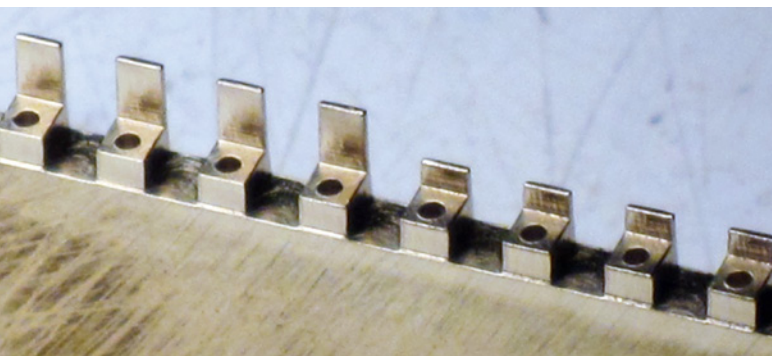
Fräsgrat mit rotierender Drahtbürste entfernt; 0,4-Millimeter-Bohrungen
